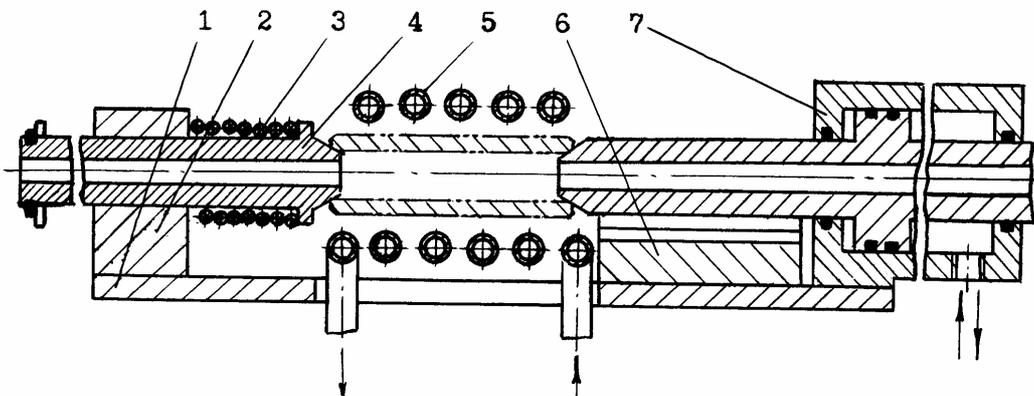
Схема станда для термопластической раздачи поршневых пальцев: 1 – плита; 2 – кронштейн; 3 – пружина; 4 – шток полый; 5 – индуктор; 6 – призма направляющая; 7 – пневмоцилиндр
